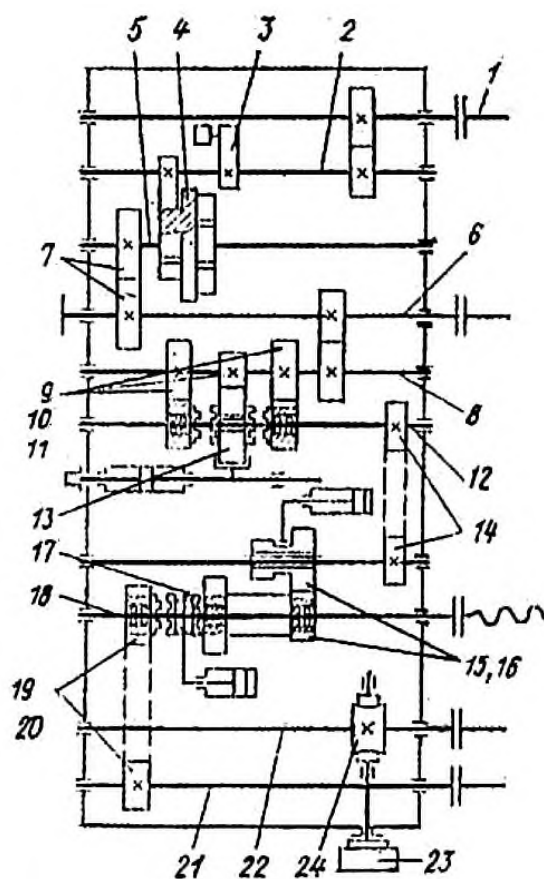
Механизм подачи и поворота заготовки [1]
